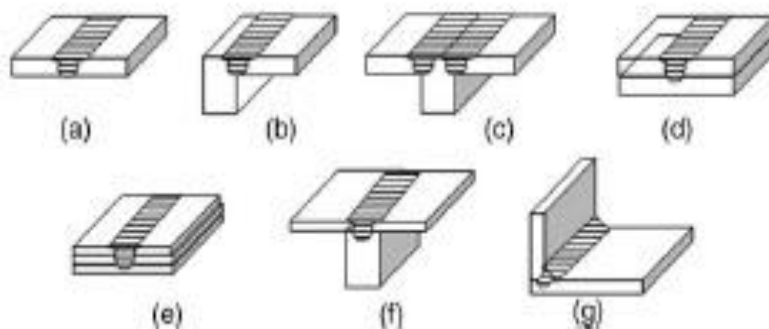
Daerah hasil pengelasan *friction stir welding
